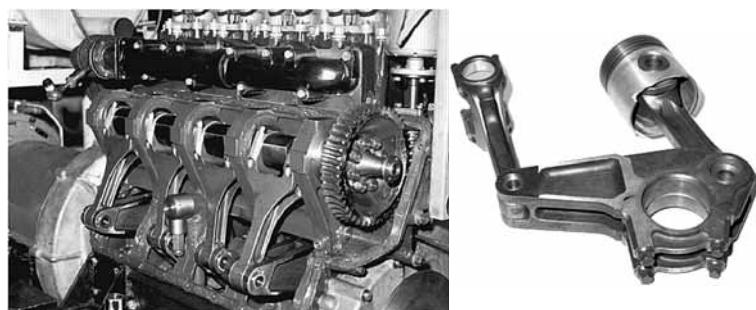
Траверсный дизель Т-01 ( $iV_h = 9,1$  л) и его детали движения на базе двигателя ЯМЗ-8424
